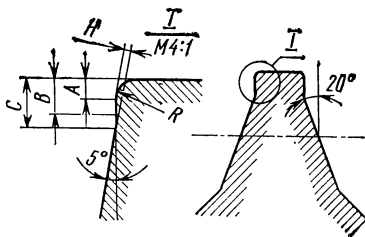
Форма профиля зуба червячной фрезы с «усиком»
